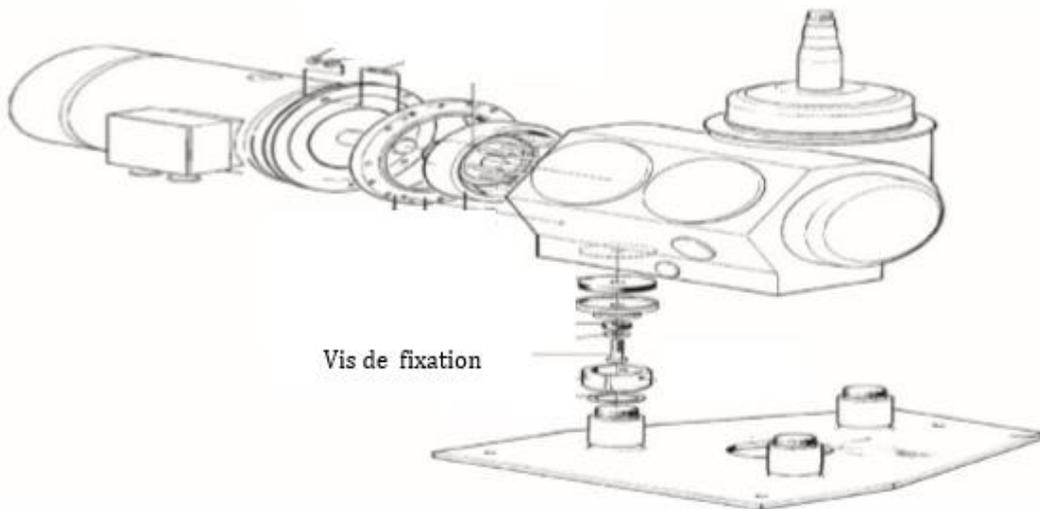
VUE ECLATE DES ELEMENTS DES PATTES DE LA MACHINE
